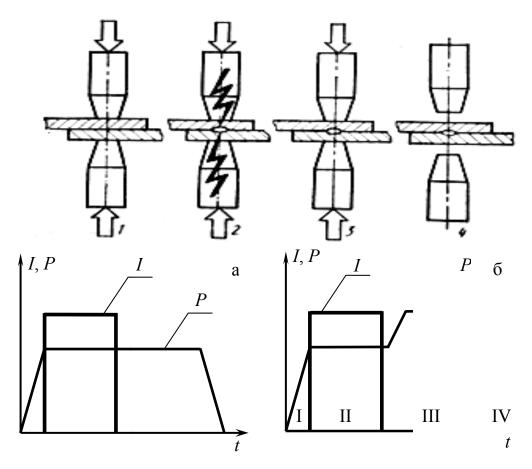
Стадии цикла и циклограммы точечной сварки: а – без увеличения давления; б – с увеличением давления при проковке (1 – сжатие деталей; 2 – пропускание тока; 3 – проковка; 4 – пауза)
